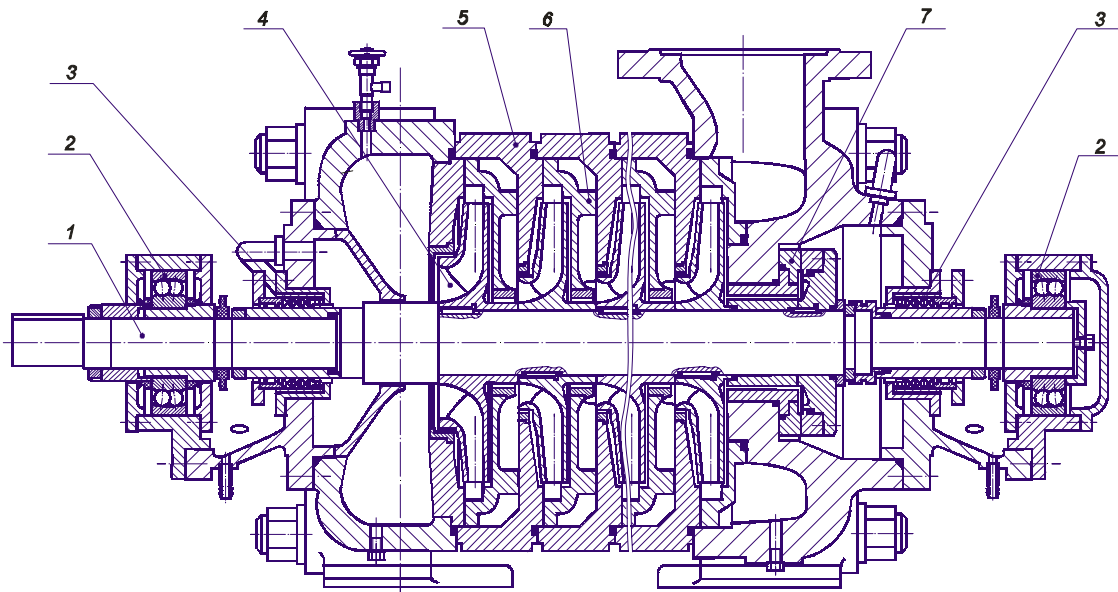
Насос ЦНСШ 300-140...800: 1 — вал; 2 — опоры качения; 3 — концевые уплотнения вала; 4 — рабочее колесо; 5 — секция; 6 — направляющий аппарат; 7 — узел гидравлической разгрузки.
